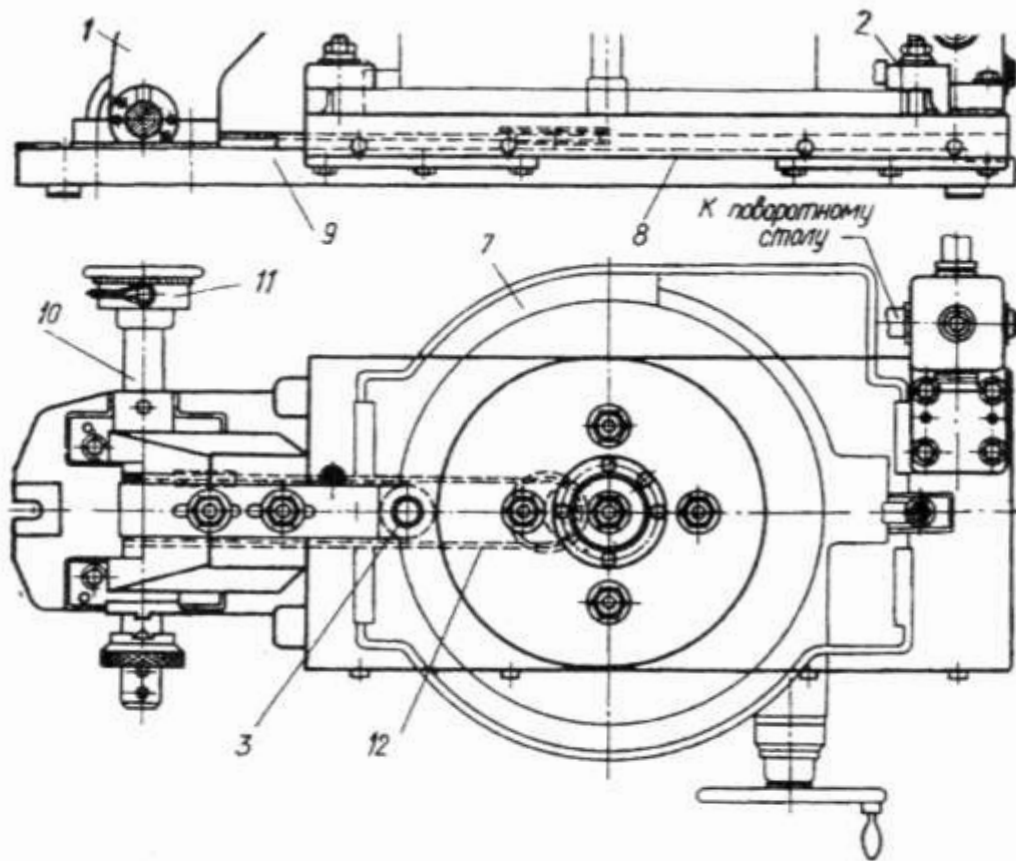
Приспособление для фрезерования профиля деталей по копиру
